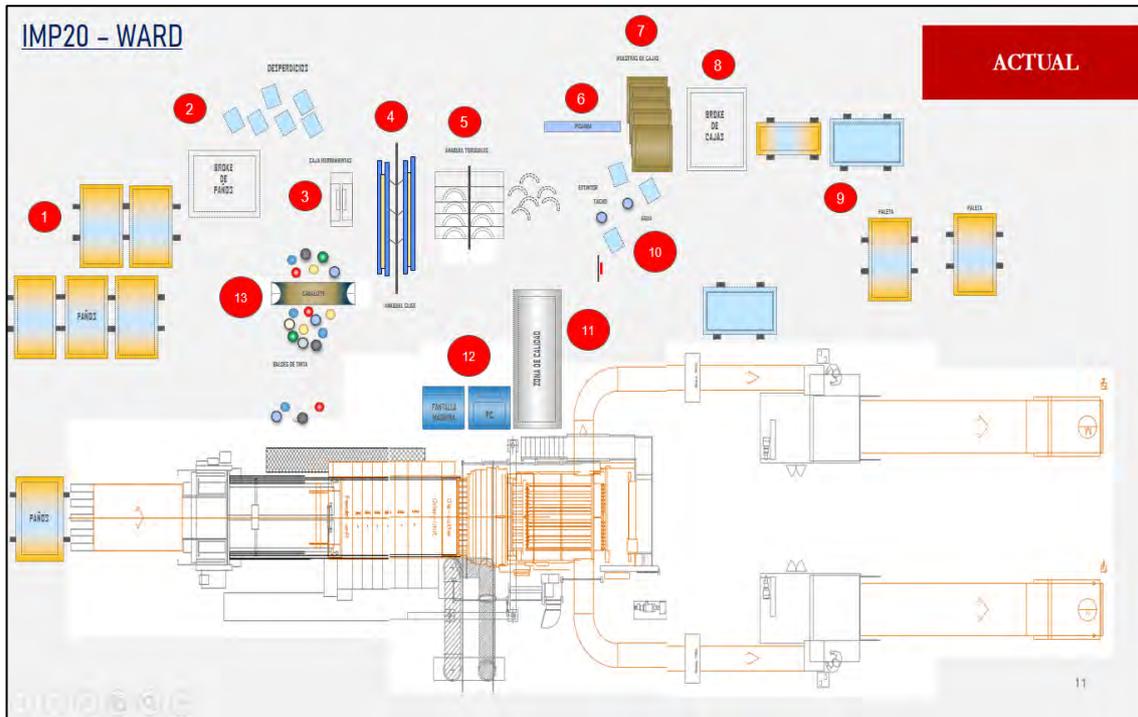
Layout zona de trabajo Imprenta 20 – Actual.
